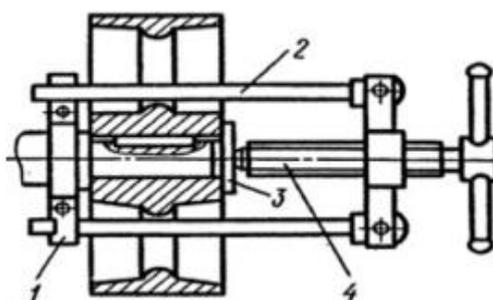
Приспособление для напрессовки шкива на вал: 1 – разъемный хомут, 2 – тяга, 3 – планка, 4 – винт.
